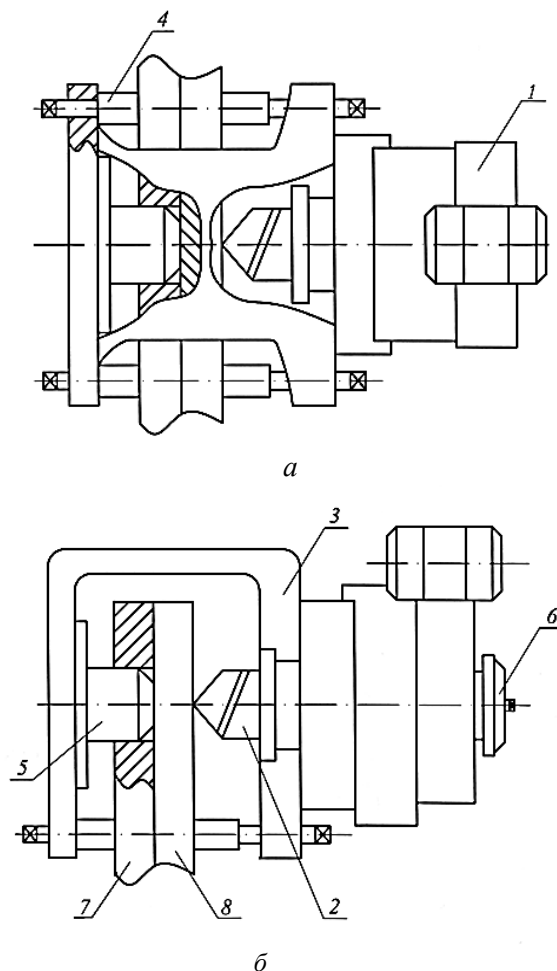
Станок для сверления и растачивания отверстий в крупногабаритных фланцевых соединениях: а – вид сбоку; б – вид сверху:
